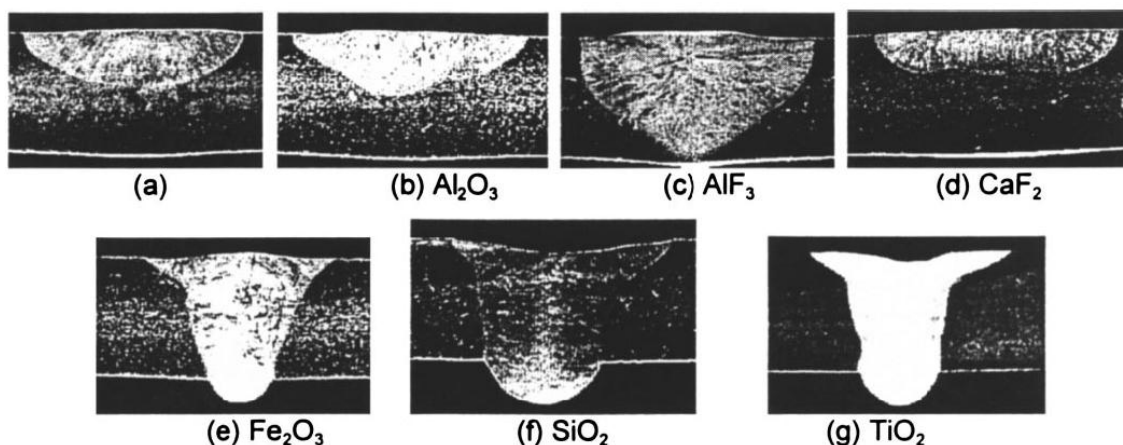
Seções transversais dos cordões de solda em chapas de 5,0mm e 220A (a) TIG convencional e (b – g) soldagem ATIG. <sup>[3]</sup>
